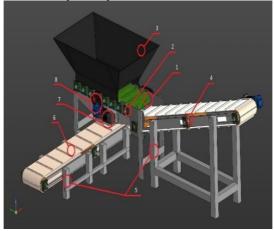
Элементы агрегата Сепаратор опилок: 1 — восьмигранные диски; 2 — подшипниковаябукса; 3 — ковш; 4 —барабан конвейера; 5 — рама; 6 — транспортерная лента; 7 — мотор; 8 — редуктор с цепной передачей
